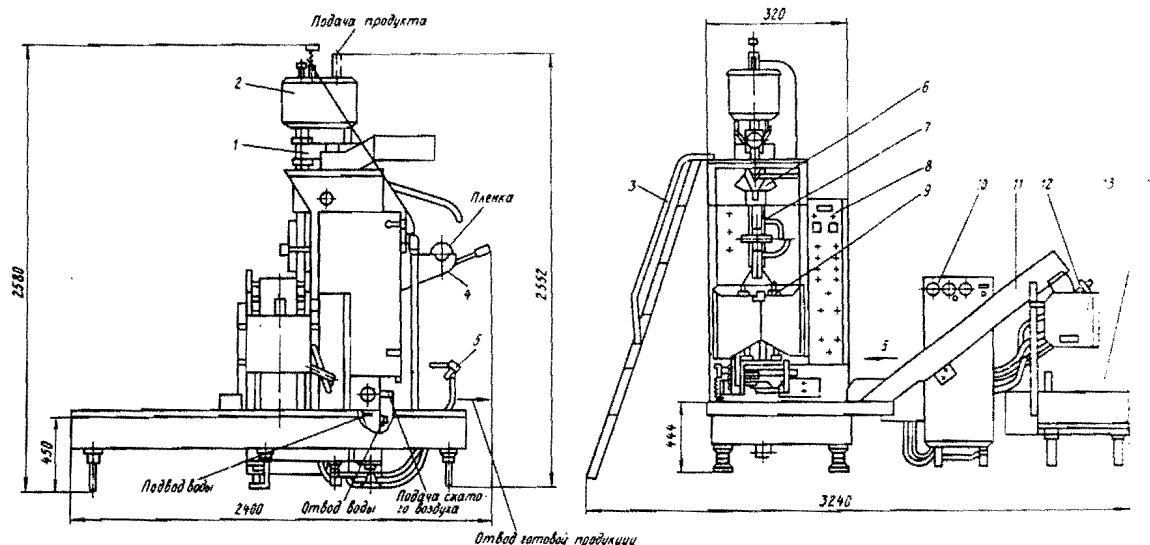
Общий вид автомата марки М6-ОРЗ-Е для розлива молока в полиэтиленовые пакеты:
